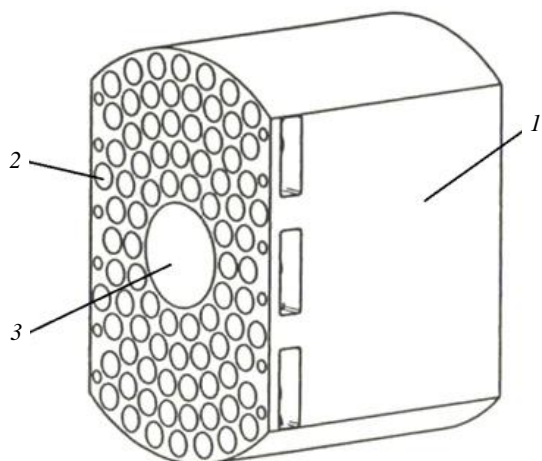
Конструкция нейтронной защиты внутри диагностического порта: 1 — поковка; 2 — стержни из карбида бора; 3 — канал для прохождения потока
